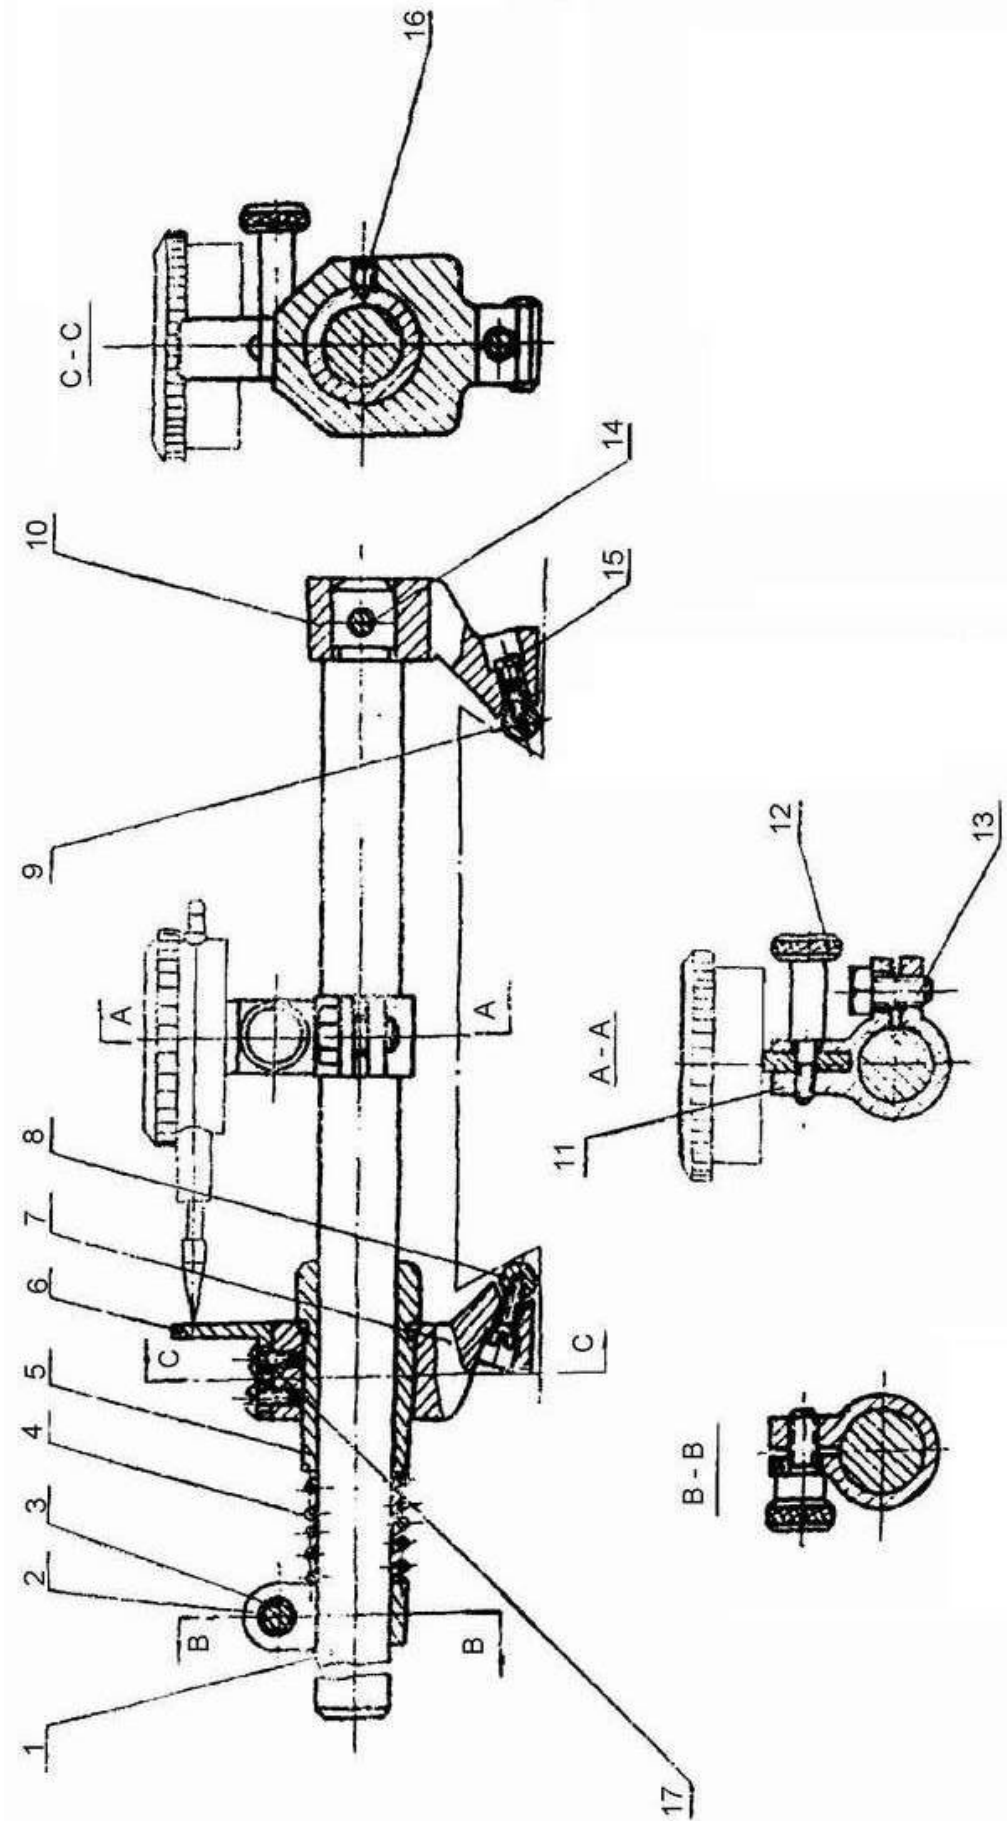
Приспособление для проверки параллельности боковых направляющих каретки суппорта
